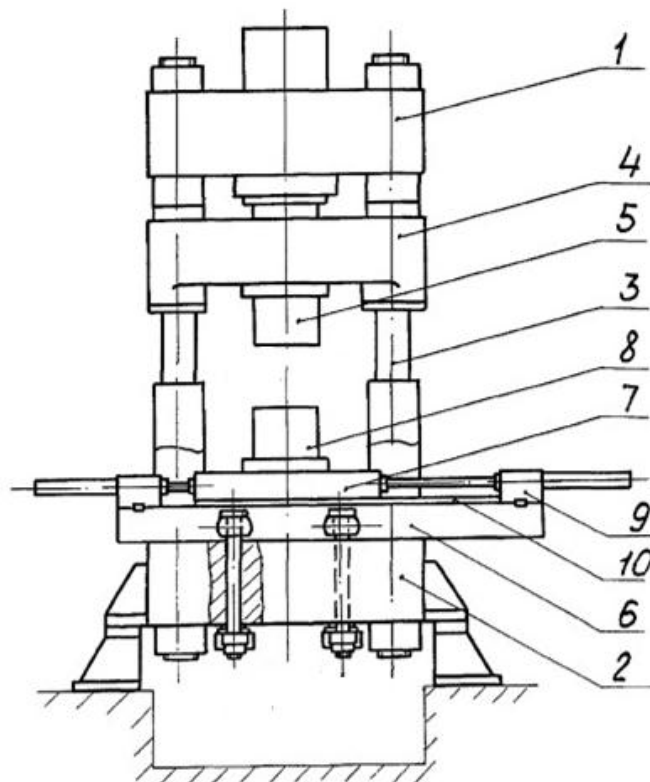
Гидравлический пресс верхнего давления. Пресс содержит: 1-верхнюю поперечина, 2-станина, 3- стянутые колонна, 4-траверс, 5-верхний инструмент, 6-промежуточная плита, 7-выдвижной стол, 8-нижний инструмент, 9-гидроцилиндр, 10-направляющий гидроцилиндра.
